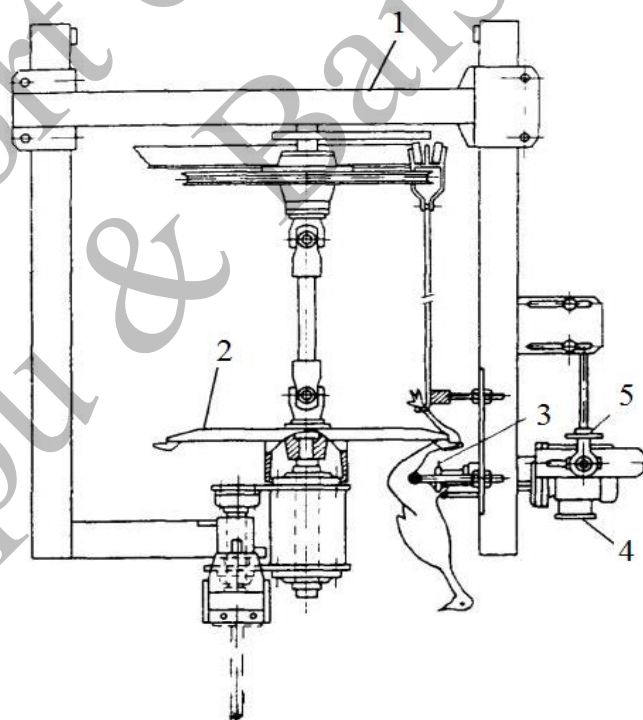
Schema mașinii pentru incizie caudală: 1- cadru suport; 2- roată ghidare; 3- cuțit disc; 4- motor electric de acționare; 5- mecanism de reglaj
